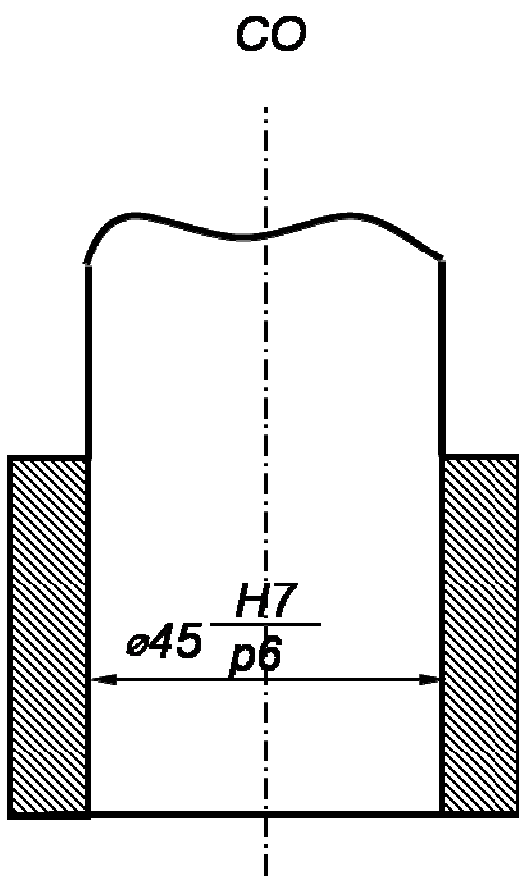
Примеры обозначения полей допусков и посадок на чертежах
